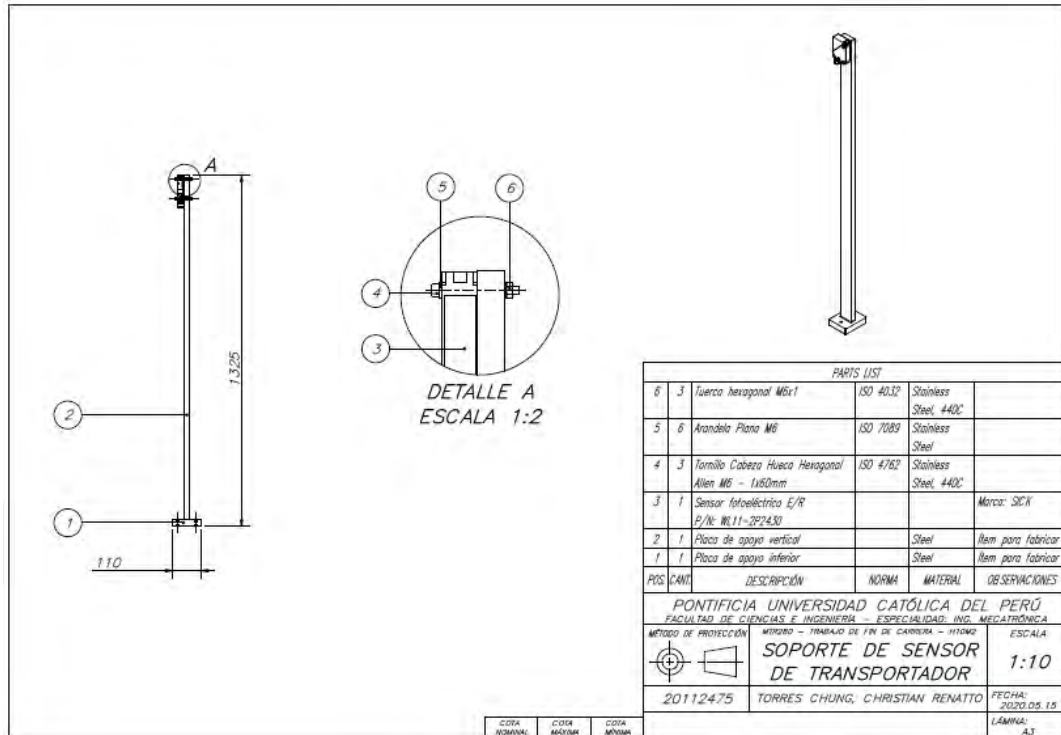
Estructura de sensor externo a transportador. Plano. Fuente: Propia.
